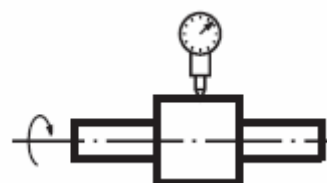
Desenho representativo da tolerância de desvio de batimento radial.
